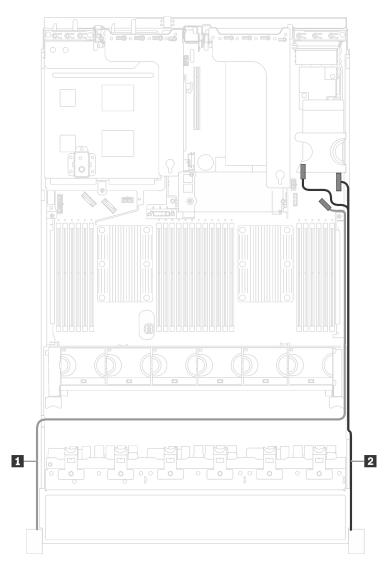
Disposición de los cables del conector VGA y el conjunto de E/S frontal en los pestillos del bastidor
